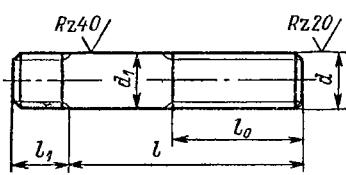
Шпильки общего применения нормальной точности для деталей с резьбовыми отверстиями
